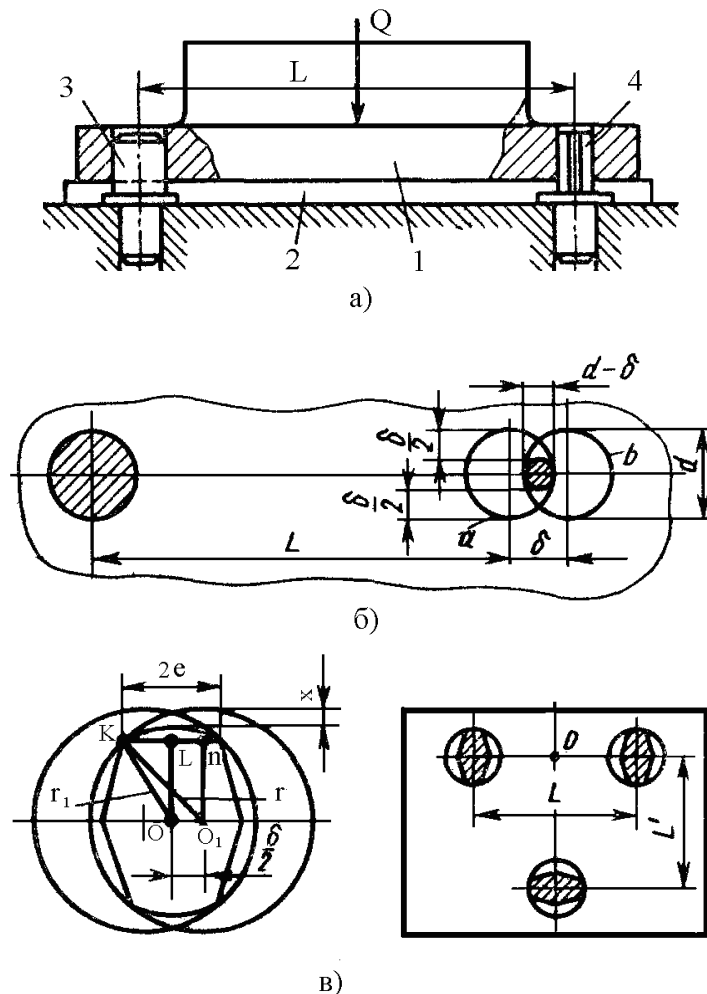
Схема встановлення заготовки базовими отворами на пальці
